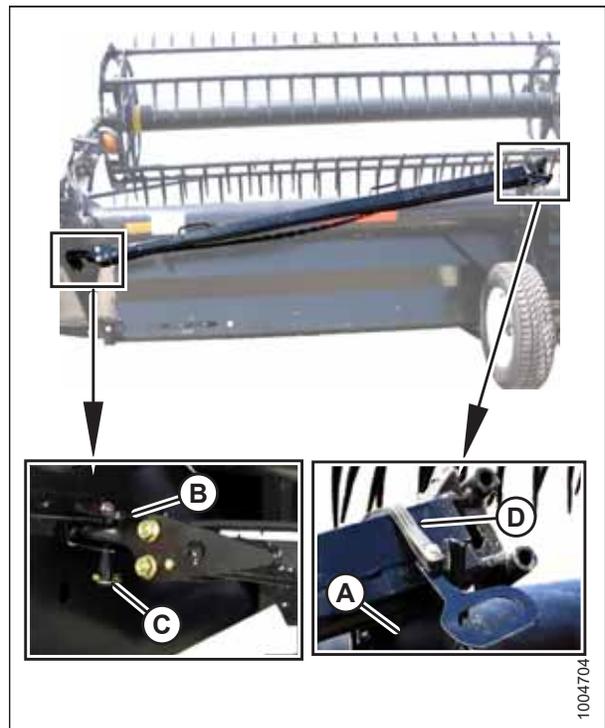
Remoção da barra de reboque – Lado esquerdo
